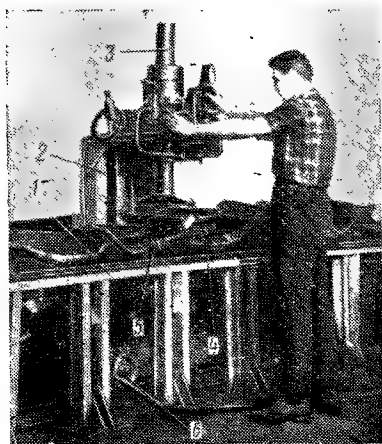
Запрессовка сердечников полюсов в катушки тяговых двигателей
